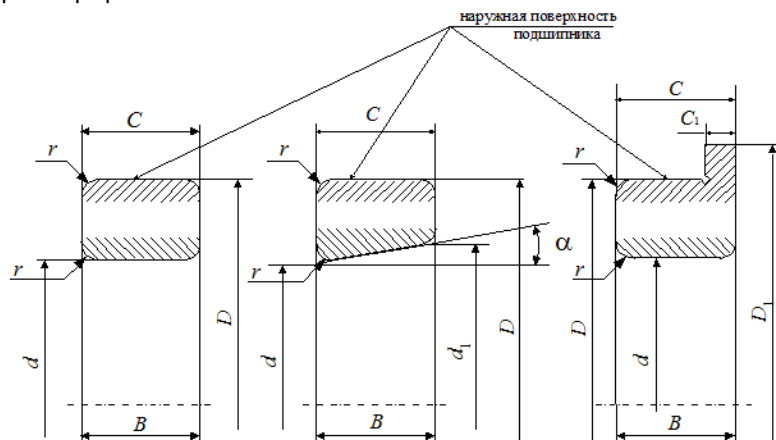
Обозначения основных размеров радиальных и радиально-упорных подшипников.
